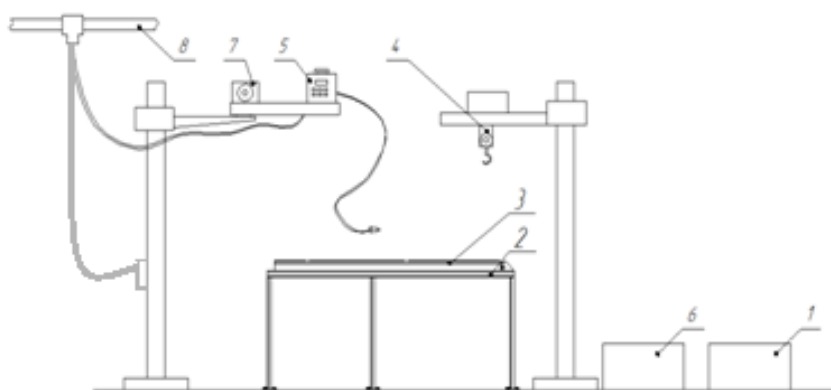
Схема компоновки рабочего места сварки узла №1:
